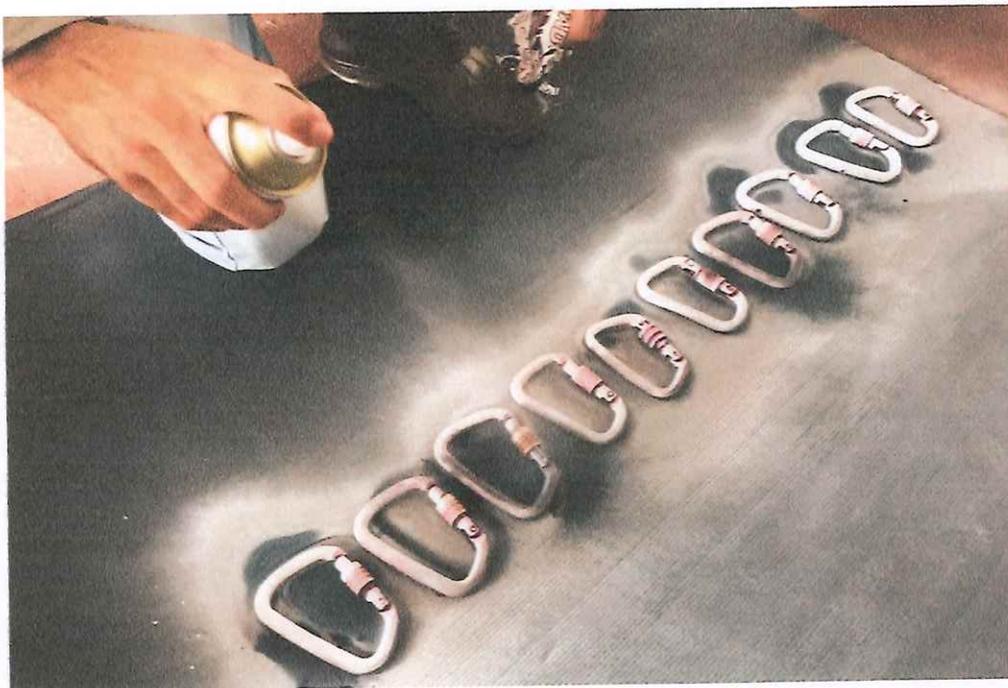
Remoção do excesso do líquido penetrante com cuidado.
